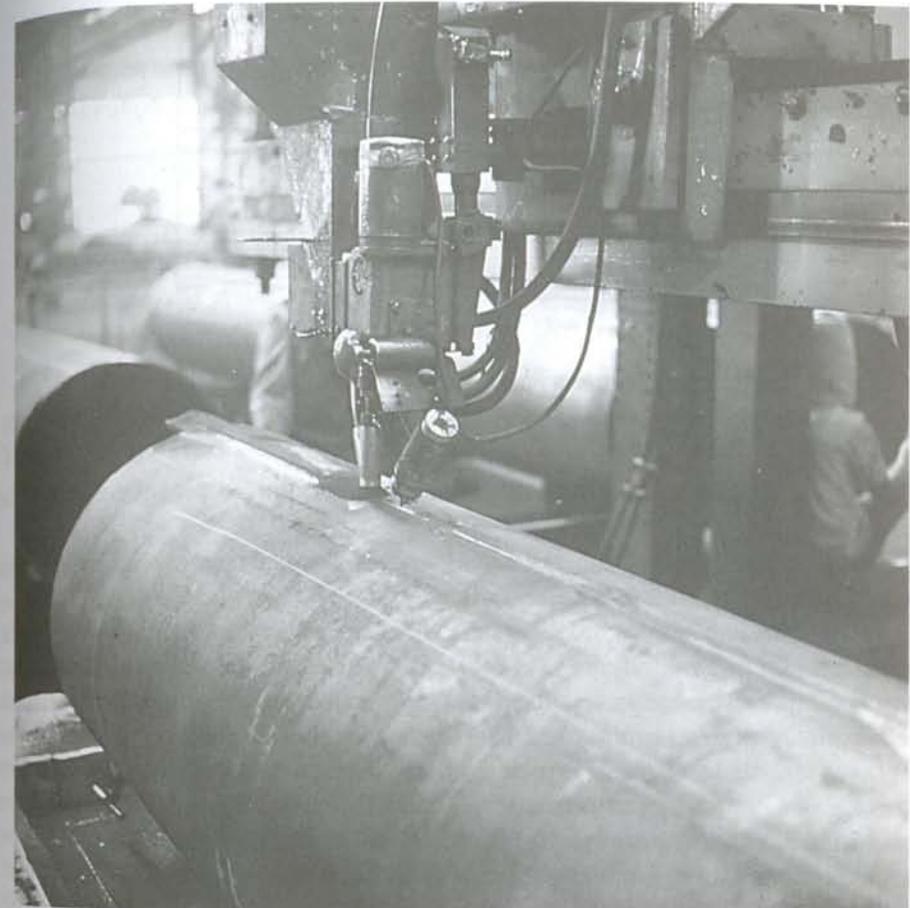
Soldagem externa de um cilindro por arco submerso. Cortesia de CONFAB Industrial S.A.
